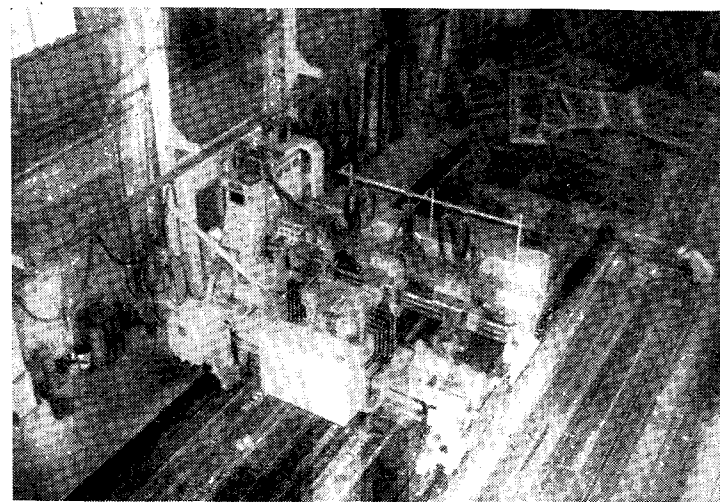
Газорезательная и маркировочная машина для резки профильной стали с цифровым управлением.
